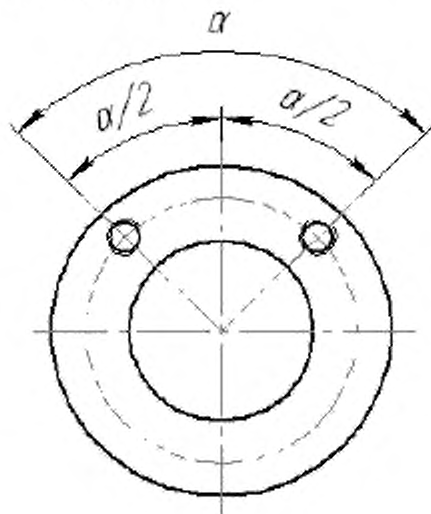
Расположение отверстий для типов соединений F03–F60
